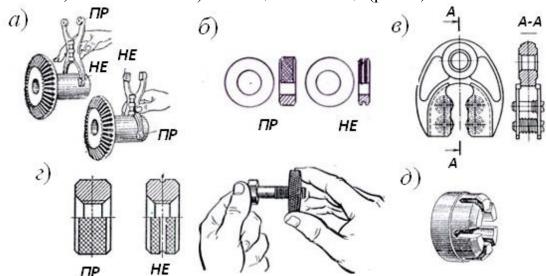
Общий вид калибров-скоб (a), калибров-колец (δ), резьбовой скобы (a), резьбовых колец (a), шлицевого кольца (a)
